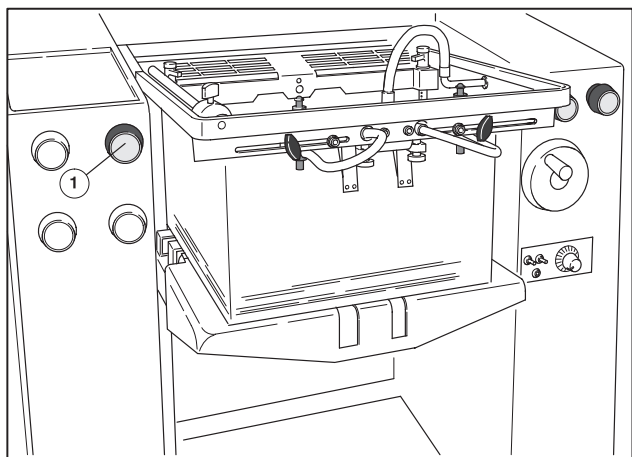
Поворотная ручка для регулировки раздува передней кромки листов
